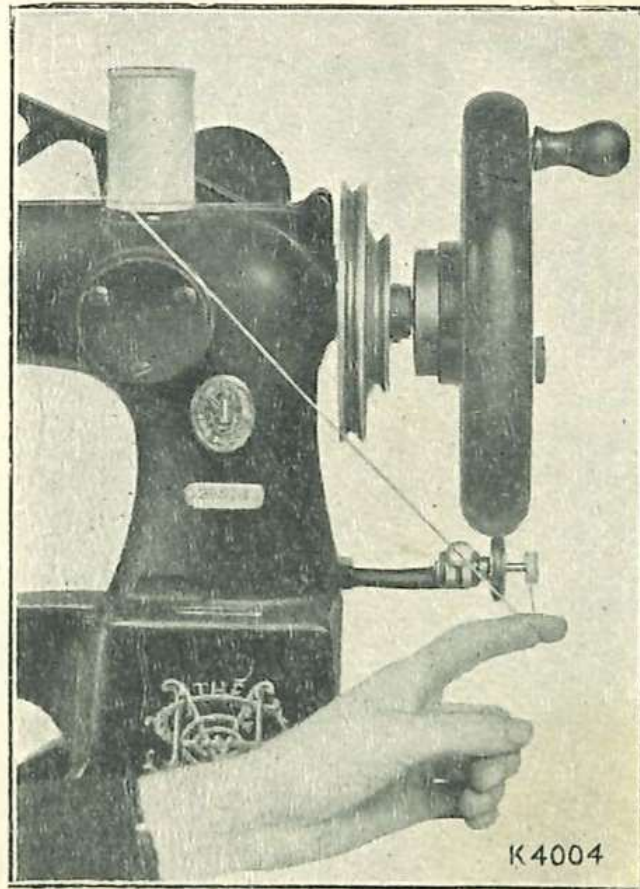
Volant et Dévidoir du Côté Poulie de la Machine.
